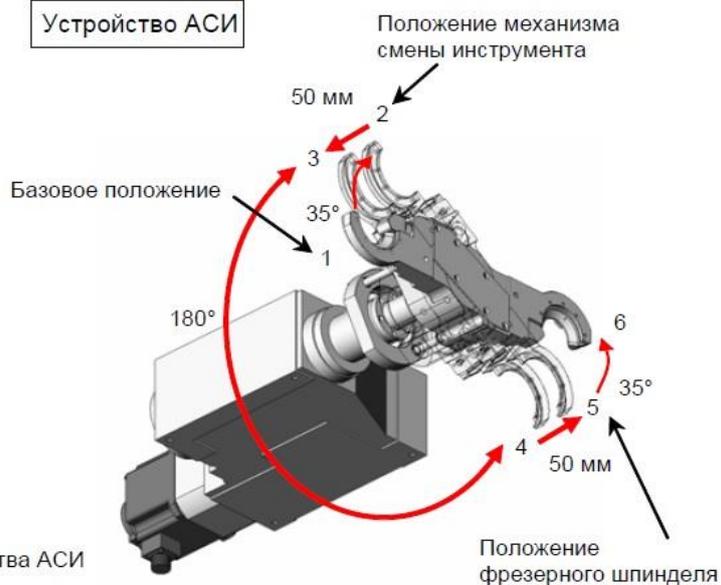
Перемещение устройства АСИ и механизма смены инструмента (для станка с магазином на 36 инструментов) [8]
